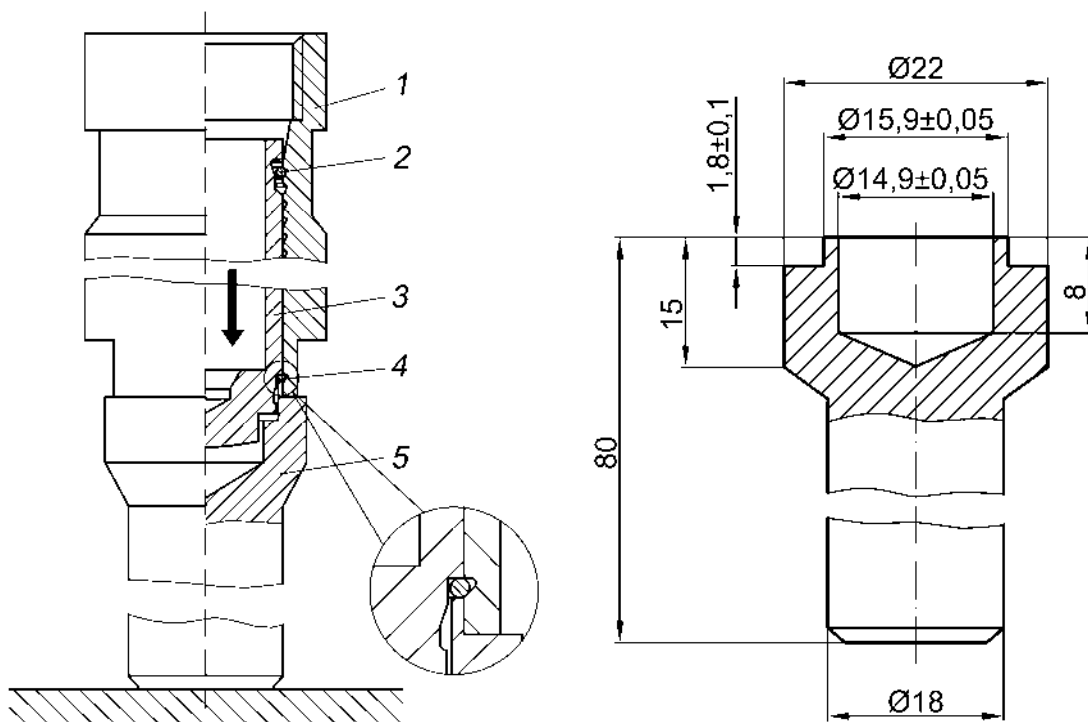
Montage des hydraulischen Spanners mit einem Dorn:
